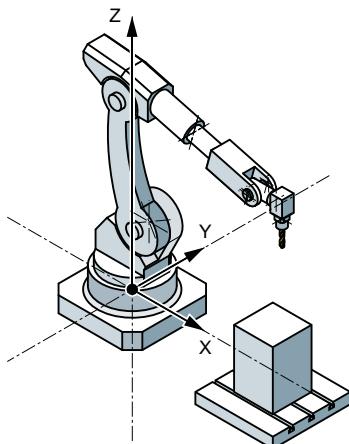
6-achsiger Knickarmroboter mit Frässpindel
